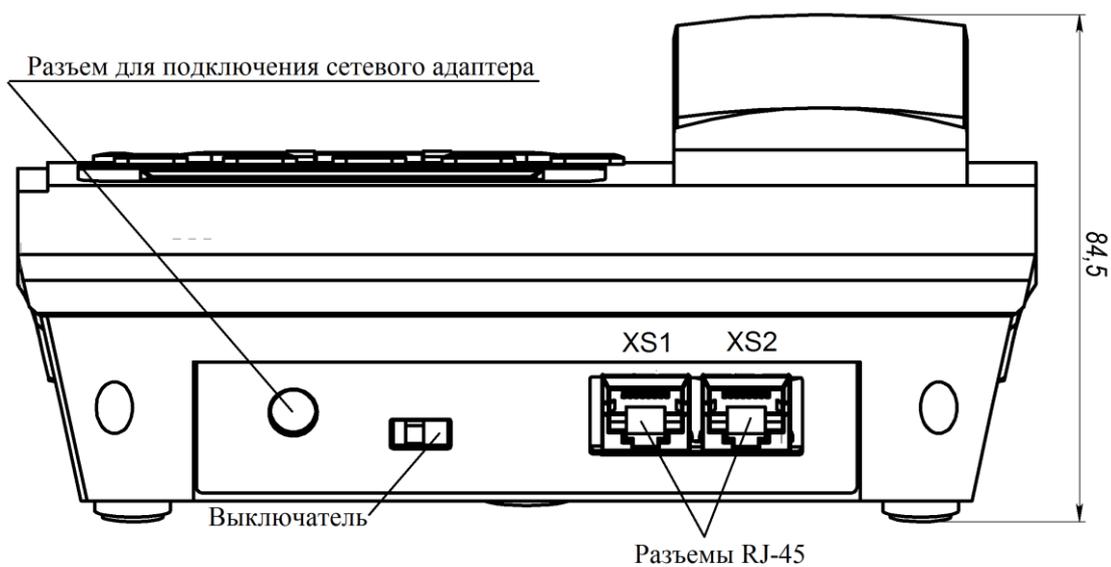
Внешний вид торцевой стороны ПД SC1000-C1
